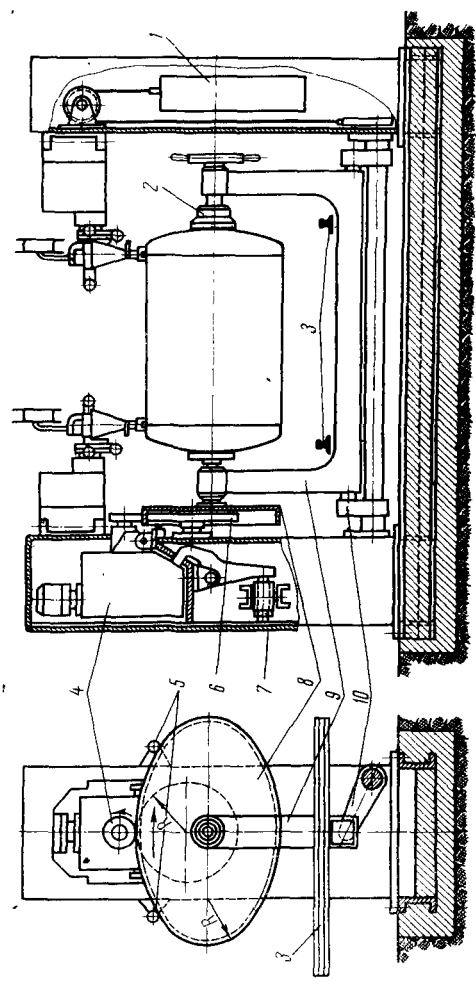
Схема станка для автоматической сварки овальных сосудов
